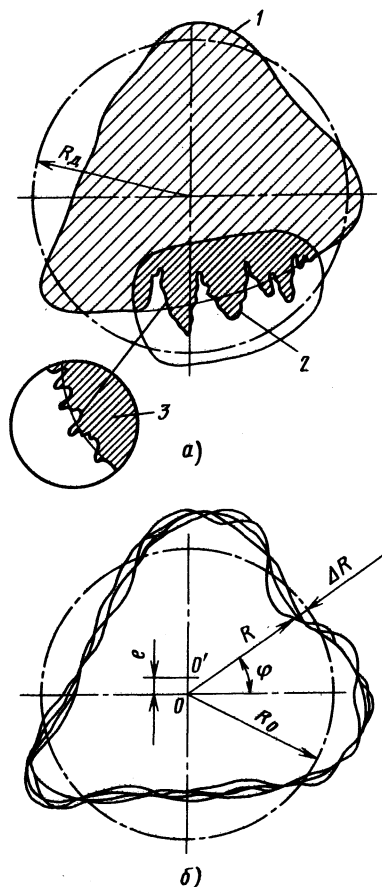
Форма поперечного сечения обработанной цилиндрической поверхности (а) и траектория движения опорной точки шпинделя (б): 1 — форма поверхности; 2 — волнистость; 3 — шероховатость; R_d — номинальный радиус обработанной детали
